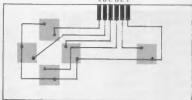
Placa para el joystick sin conector. Los cables han de ir soldados en los seis contactos que hay en la parte superior.
